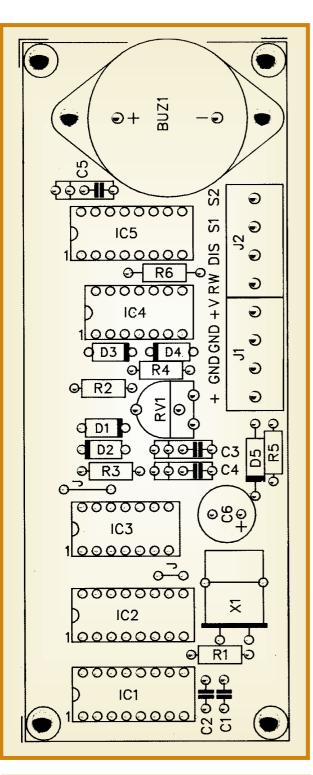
Lado de los componentes de la plaqueta principal.
